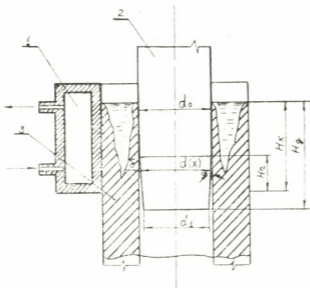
Схема непрерывного литья полый заготовки: 1 — кристаллизатор, 2 — дорн, 3 — заготовка
